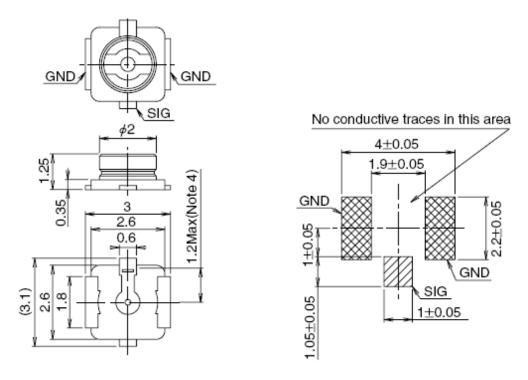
U.FL-R-SMT 连接器尺寸(单位: 毫米)
